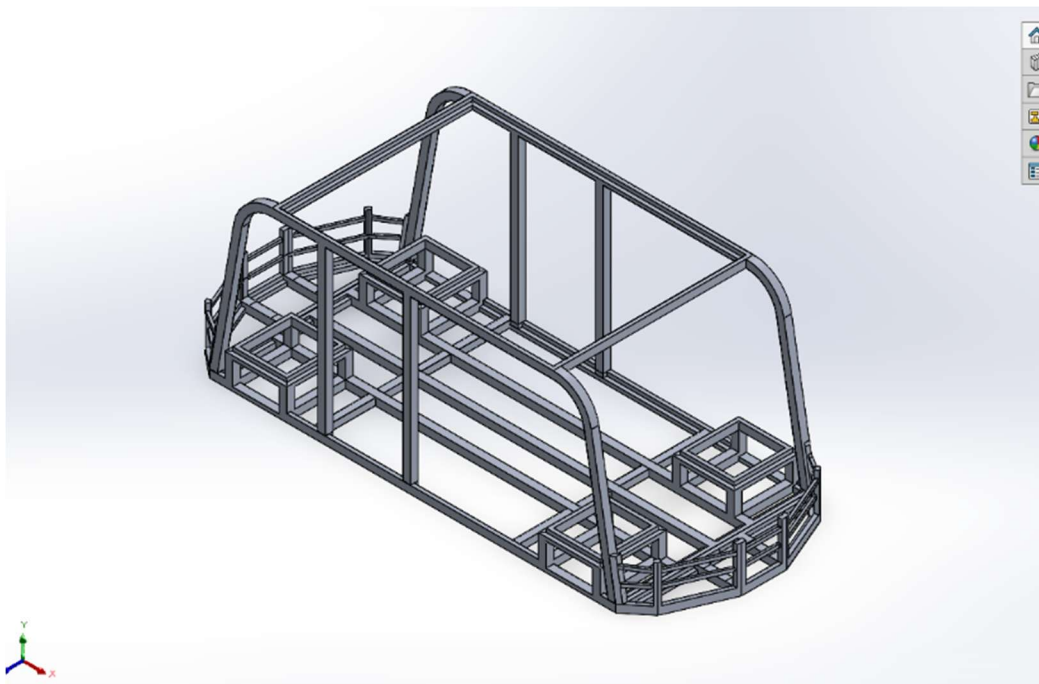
Rediseño de la distribución de los perfiles de la estructura “space frame”.
